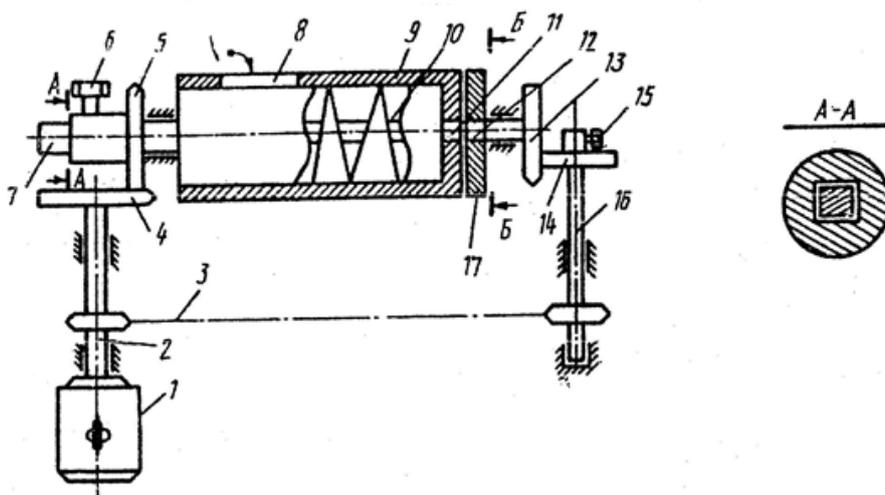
Схема передаточного механизма, устройства для формования полуфабрикатов кондитерских изделий
